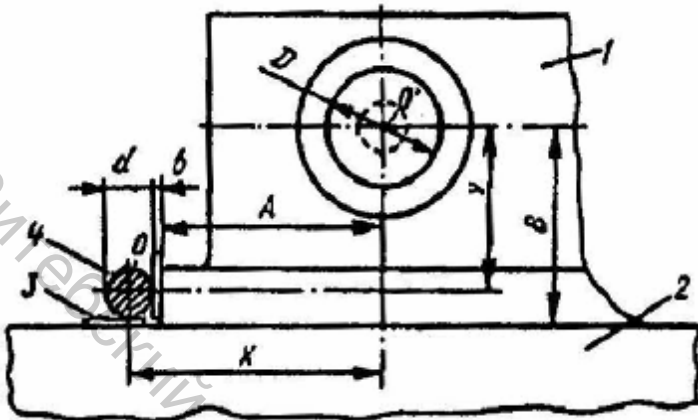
Схема настройки на размеры A и B от технологических баз с помощью шкал и лимбов приводов перемещений горизонтально-расточного станка для растачивания отверстия
